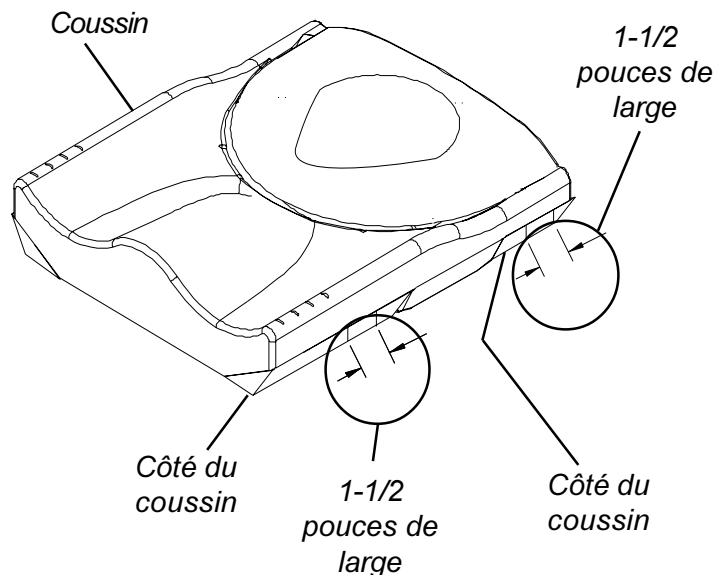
MODIFIER LE COUSSIN POUR UNE PLAQUE DE SIÈGE SURBAISSÉE
